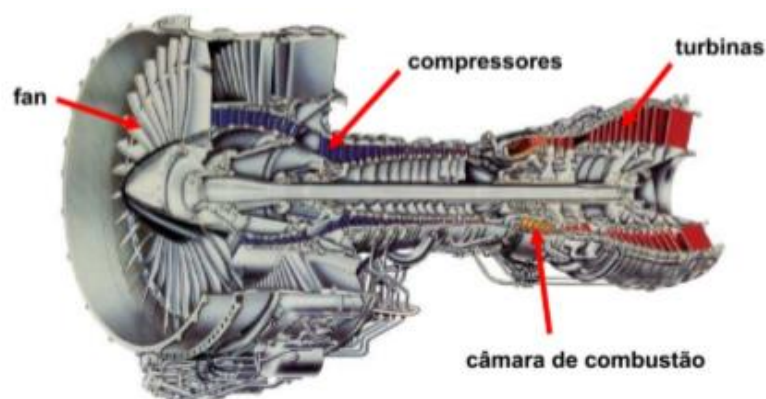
Motor *Turbofan* e seus principais componentes [46].
